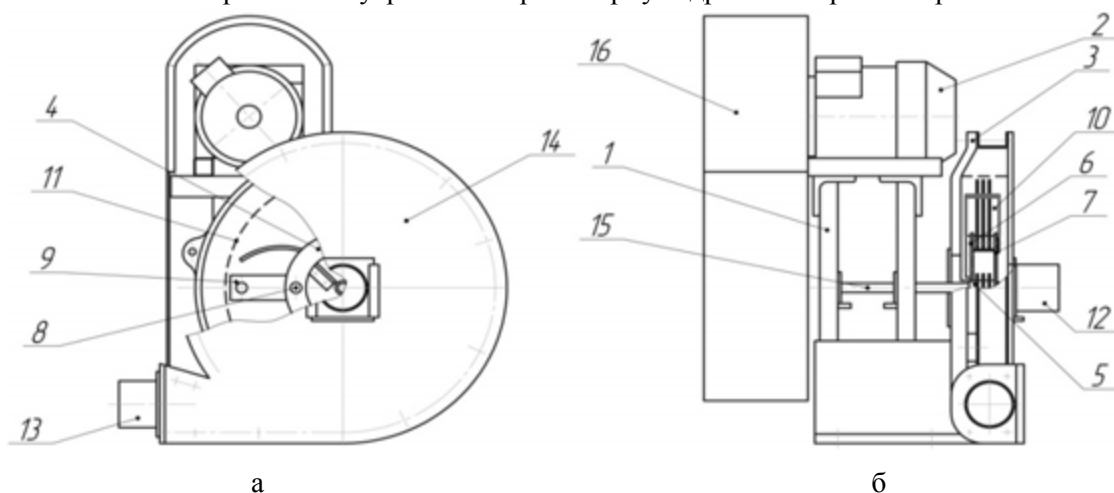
Конструктивное устройство экспериментальной молотковой дробилки с ротором-вентилятором: а – общий вид; б – вид сбоку; 1 – рама; 2 – электродвигатель; 3 – корпус; 4 – ротор-вентилятор; 5 – ступица; 6, 7 – соответственно внутренний и наружный диски; 8 – ось подвеса; 9 – набор молотков; 10 – лопатки вентилятора; 11 – решето; 12 – всасывающий патрубок; 13 – выгрузной патрубок; 14 – крышка; 15 – вал; 16 – кожух
